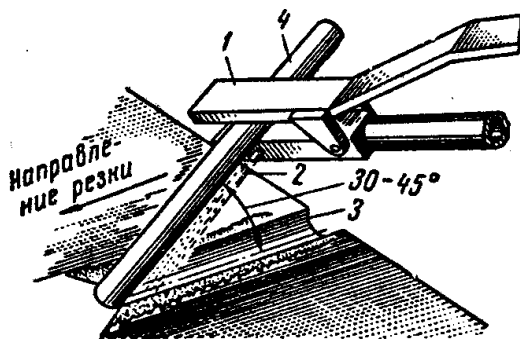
Схема процесса воздушно-дуговой резки:
